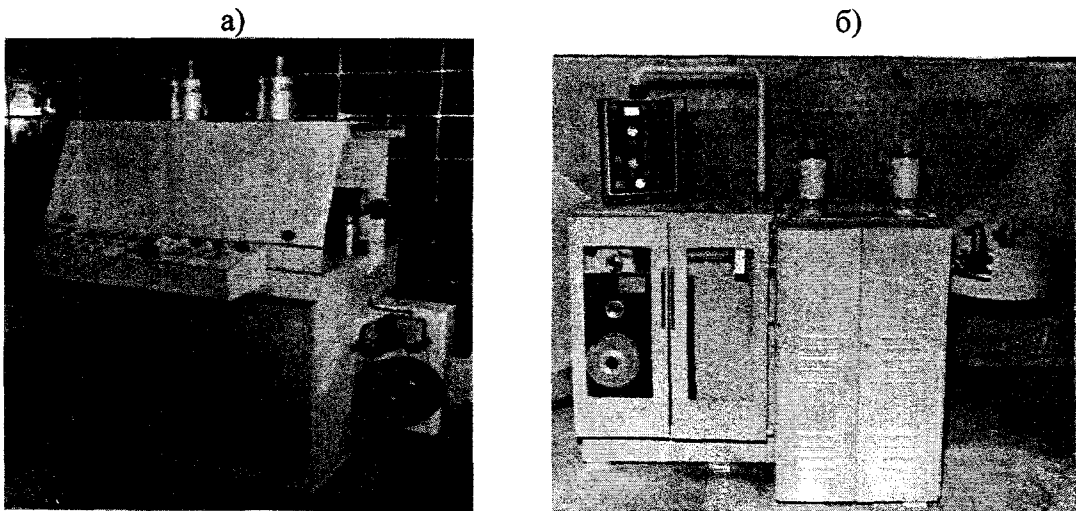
Общий вид станков для магнитно-абразивной обработки проволоки модели 922 (а) и 8.013 (б)
